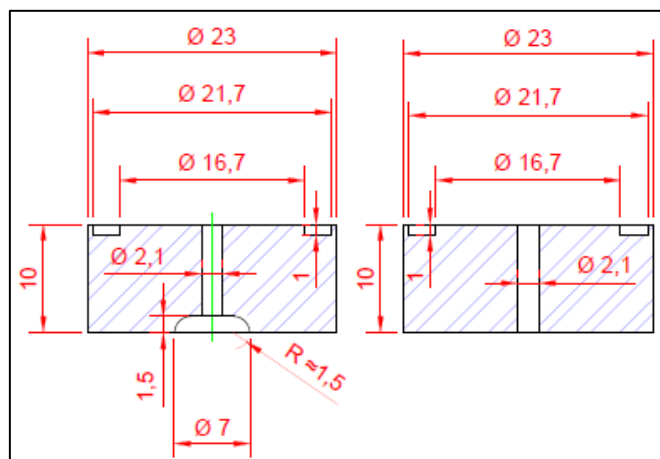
Desenho em AutoCAD 2013 do corte da vista frontal de um conjunto porta amostra para o capilar de 1,3 mm.
